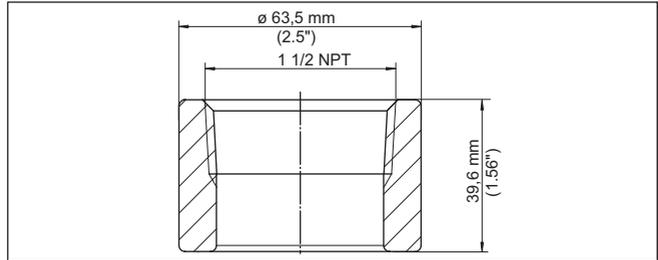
Dimensiones racor para soldar rosca 1 1/2 NPT (ASME B 1.20.1)
